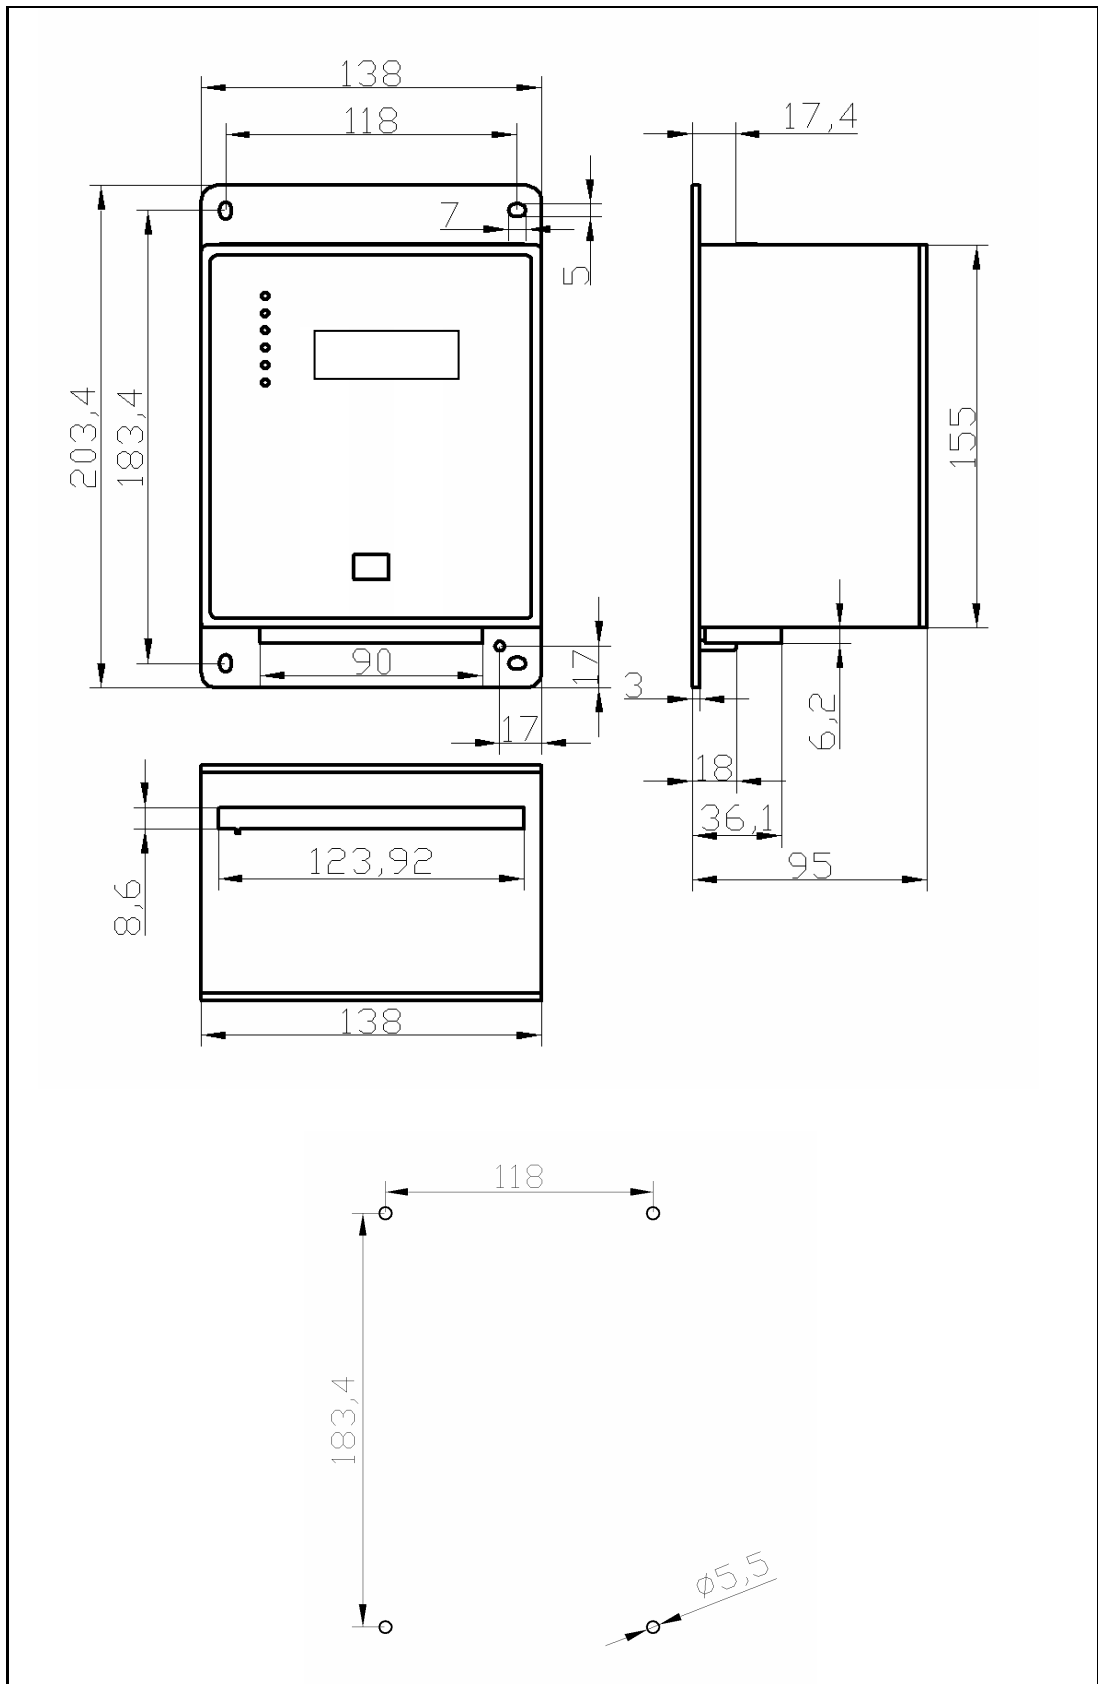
Размеры. Корпус P115 для настенного монтажа
